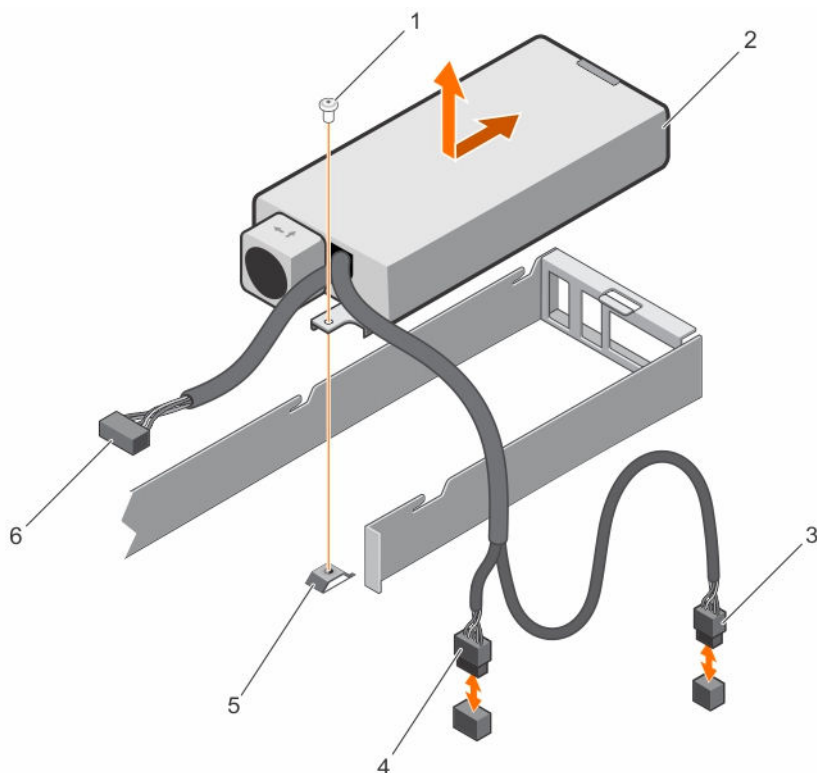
Remover e instalar uma fonte de alimentação com cabo
